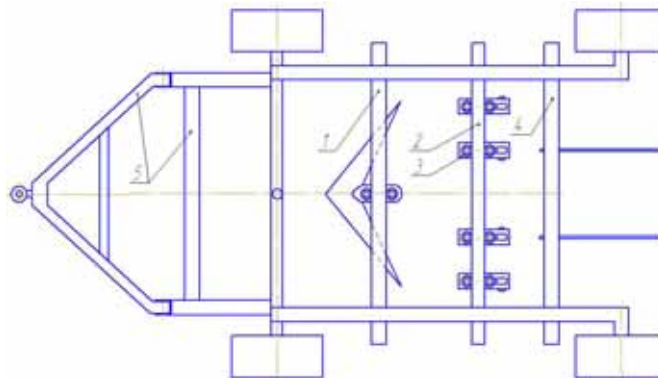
Положення робочих органів і основних елементів лабораторно-польової установки (вид зверху):
